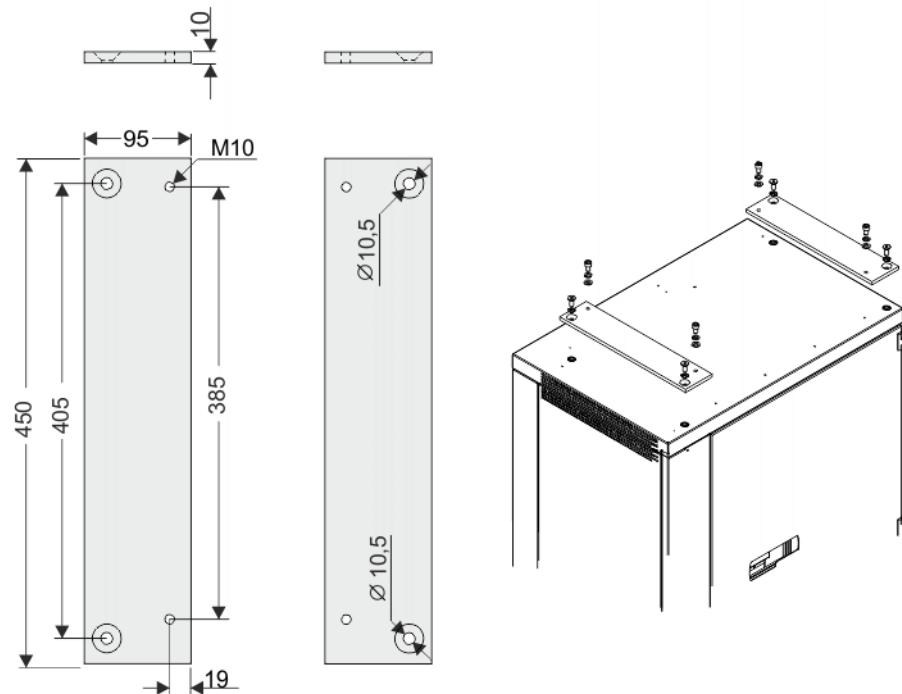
Armario de soldadura, fijación a los rieles de adaptación
